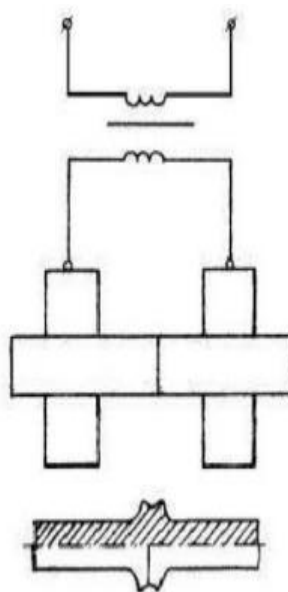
Схема контактно стыковой сварки сопротивлением
